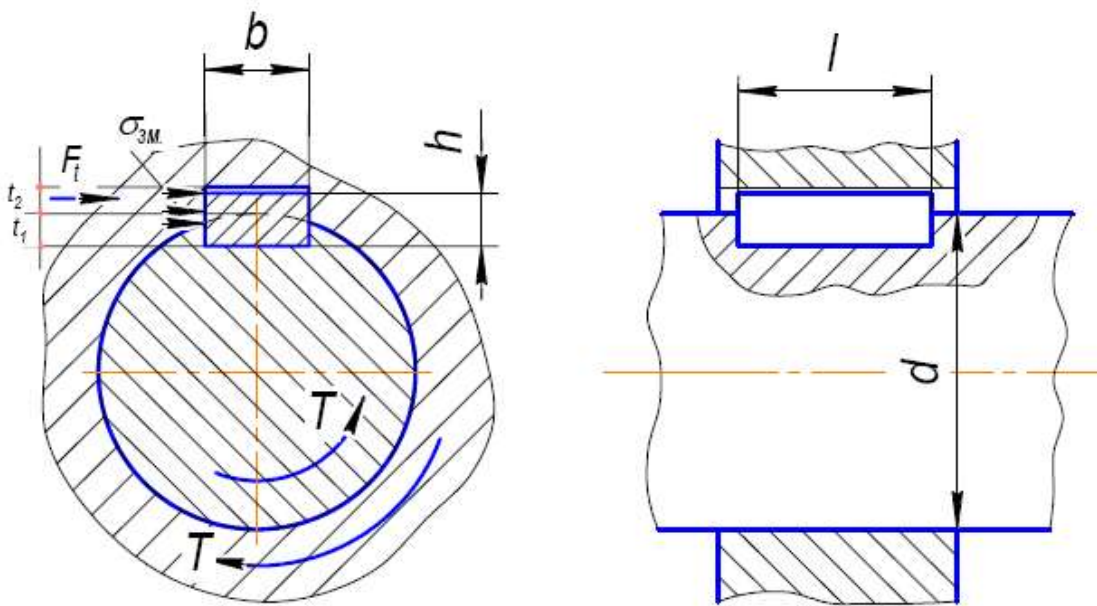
Схема сил, що діють на шпонкове з'єднання привідного вала з шестернею
